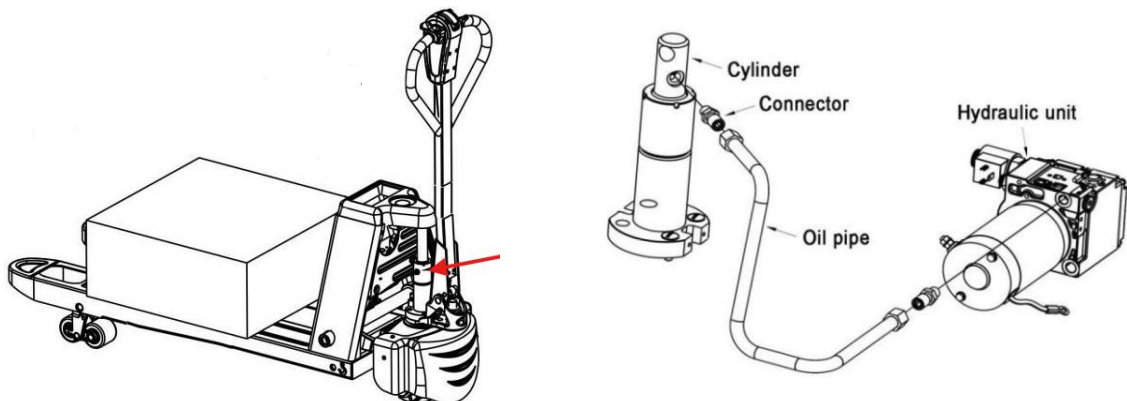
Bilderklärung Hydrauliköl Wechsel
